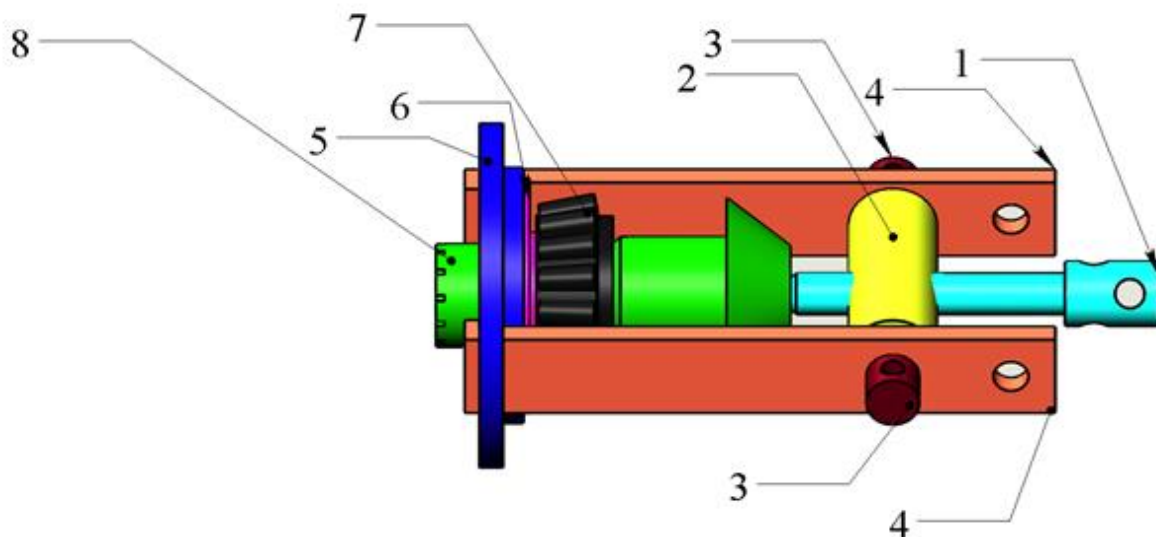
Модель запрессовки внутреннего кольца заднего подшипника: 1-винт, 2-траверса, 3-торцевой винт, 4-тяга, 5-обойма, 6- вкладыш, 7 - внутреннее кольцо подшипника 6-7807у в сборе, 8 – вал.
